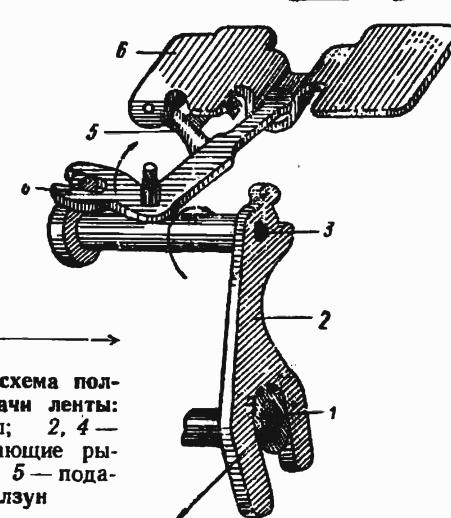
Конструктивная схема ползункового механизма подачи ленты:
